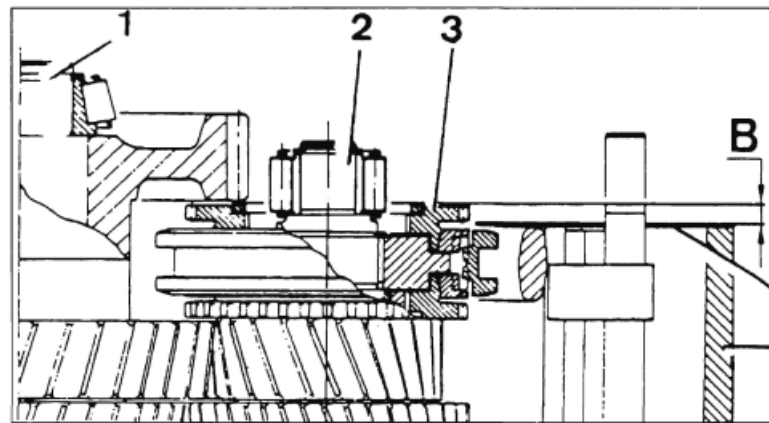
Вимірювання розміру «В» для вторинного вала:
